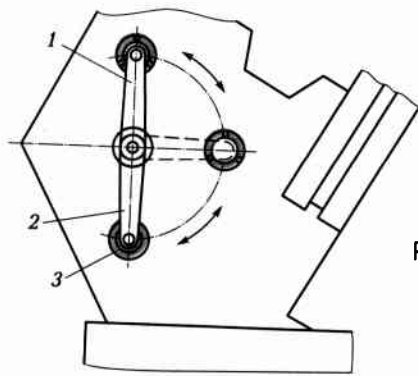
Манипулятор для автоматической установки и съема штучных заготовок на токарно-револьверном станке с ЧПУ
